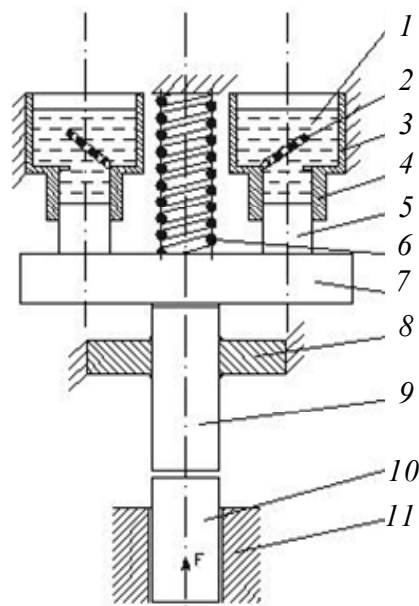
Антидриблинговое устройство с отскакивающим грузом: 1 – масло; 2 – клапан с фильерными отверстиями; 3 – резервуар; 4 – цилиндр; 5 – поршень; 6 – возвратная пружина; 7 – груз; 8 – фланец; 9 – неподвижный контакт; 10 – подвижный контакт; 11 – направляющая втулка
